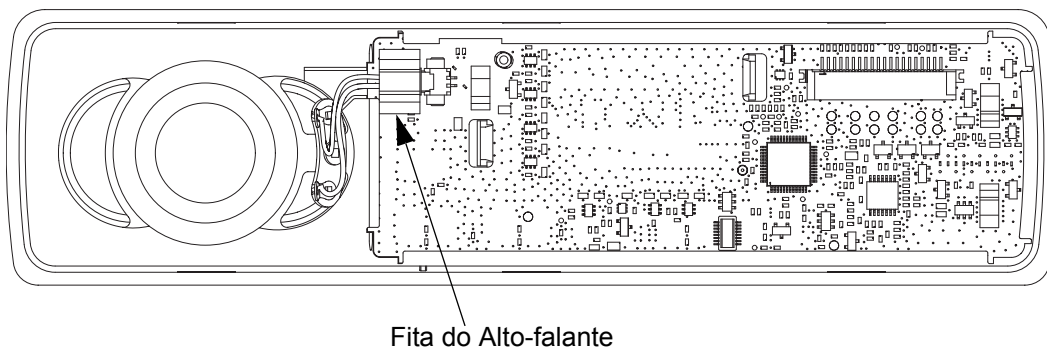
Montagem da Fita do Alto-falante na PCB
